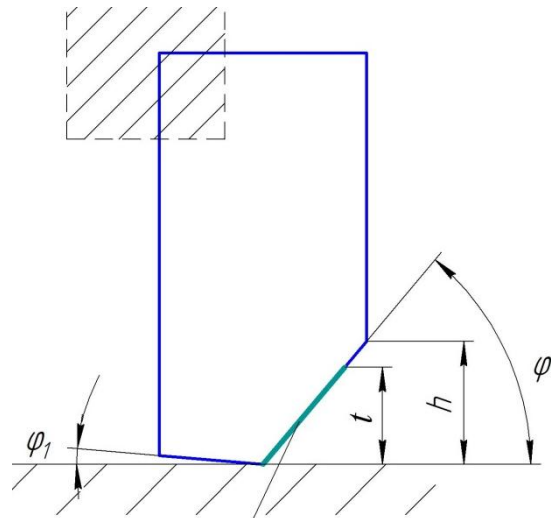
Профиль зуба фрезы: φ – главный угол в плане; φ_1 – вспомогательный угол в плане; h – высота угловой режущей кромки; t – глубина резания
